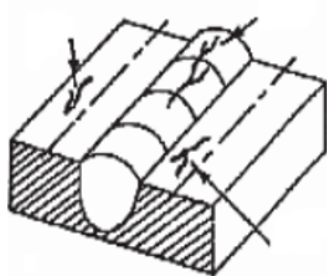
Эскиз дефекта сварного шва
